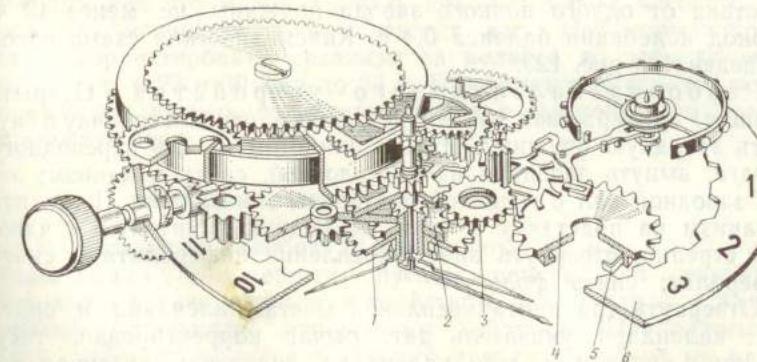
Кинематическая схема календарного устройства часов «Полет» 2414:
